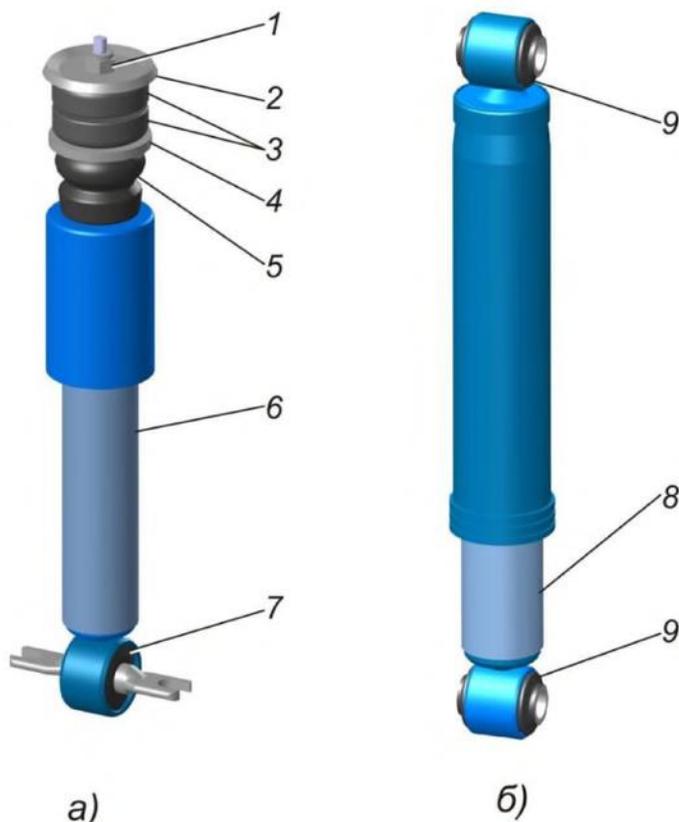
Амортизаторы: а - передний; б - задний; 1- гайка; 2,4 -шайбы; 3 - подушки; 5 - буфер сжатия; 6,8 – амортизаторы; 7,9 – резинометаллические шарниры
